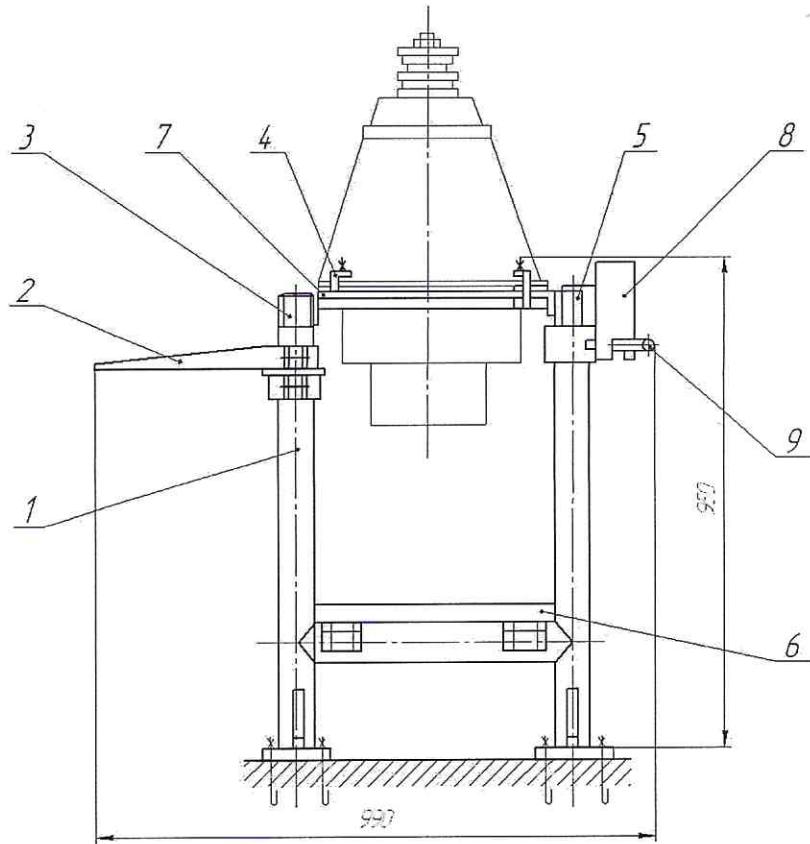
Схема стенда модели 3022 для разборки и сборки редуктора заднего моста: 1-основание; 2-полка; 3,5-подшипники; 4-откидной зажим; 5-тяга; 6-поддон; 7-поворотный стол; 8-механизм поворота; 9-рукоятка.
